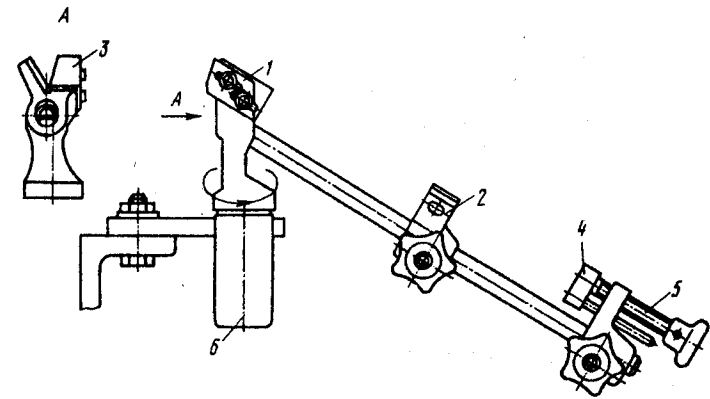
Приспособление для заточки сверла с цилиндрической задней поверхностью
